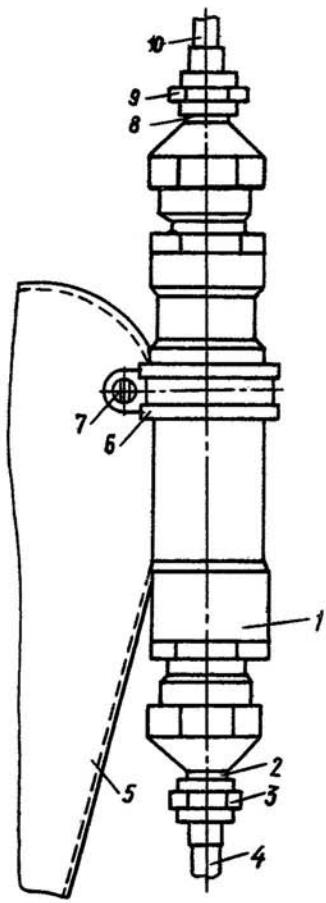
Установка предохранительного клапана ГА-42-00-ЗК:
